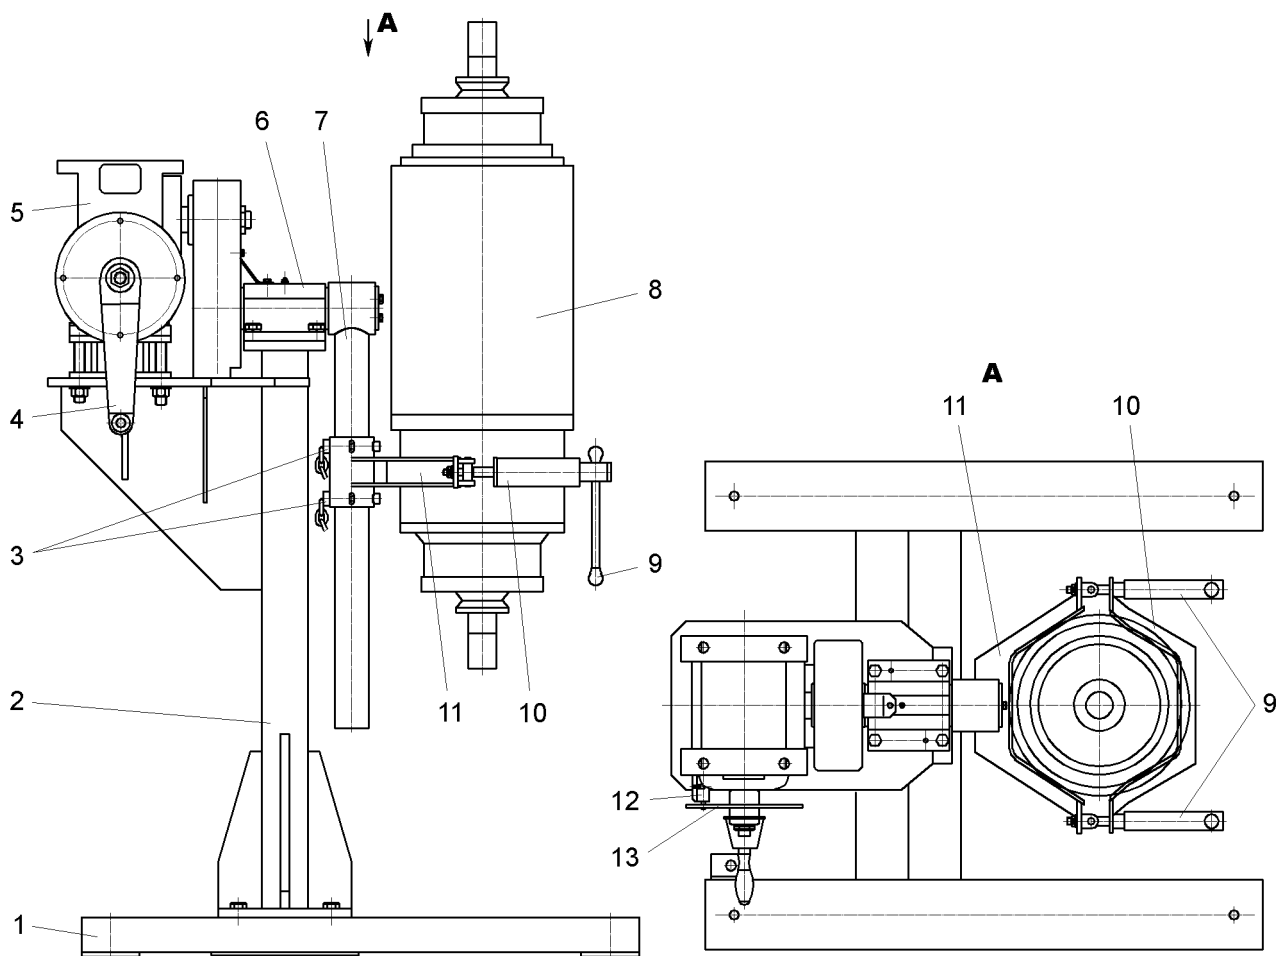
Кантователь для разборки и сборки цилиндров пневмогидравлической подвески:
